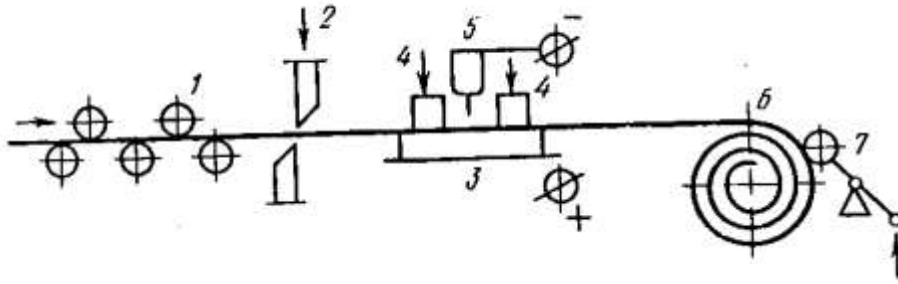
Схема линии для аргоно-дуговой сварки:
